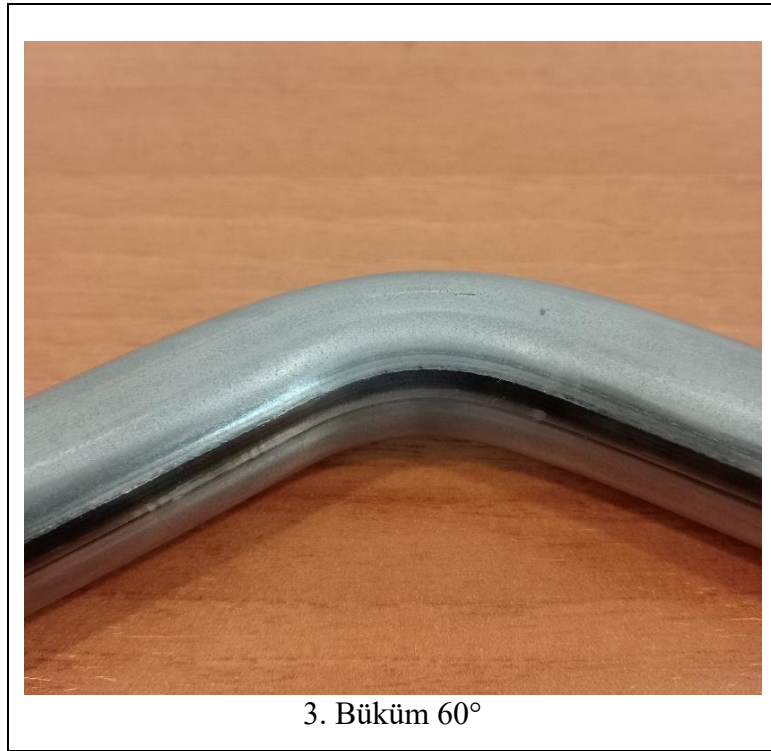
Dynaform kalınlık büküm görselleri 30° – 45° - 60° - 75° - 90° (devam)
